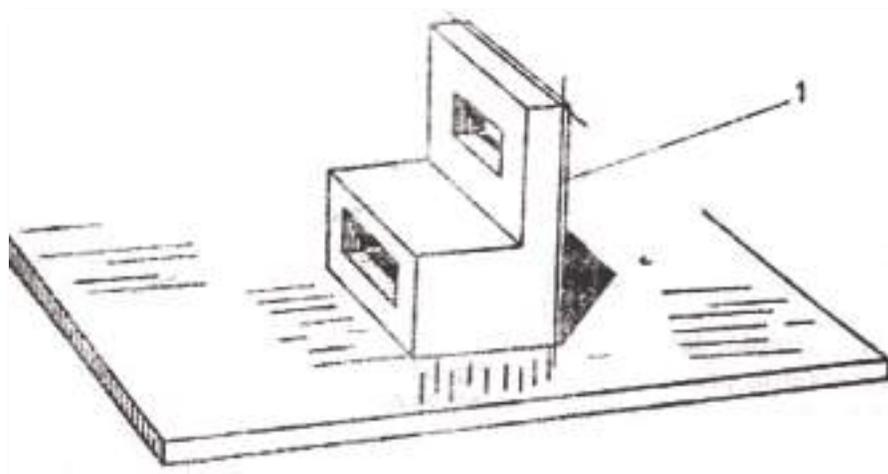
Colocação da peça para a traçagem de um plano perpendicular ao plano horizontal (1).
